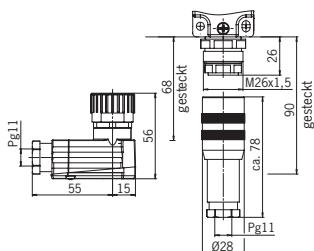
Maßzeichnung NZ2VZ-5... mit Steckverbinder SR11
